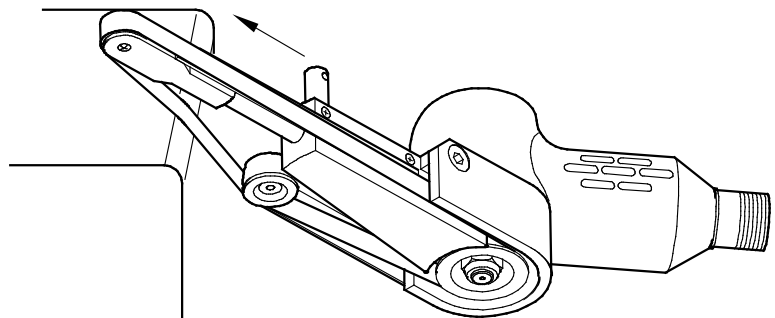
Radien bearbeiten (Symbolzeichnung)
